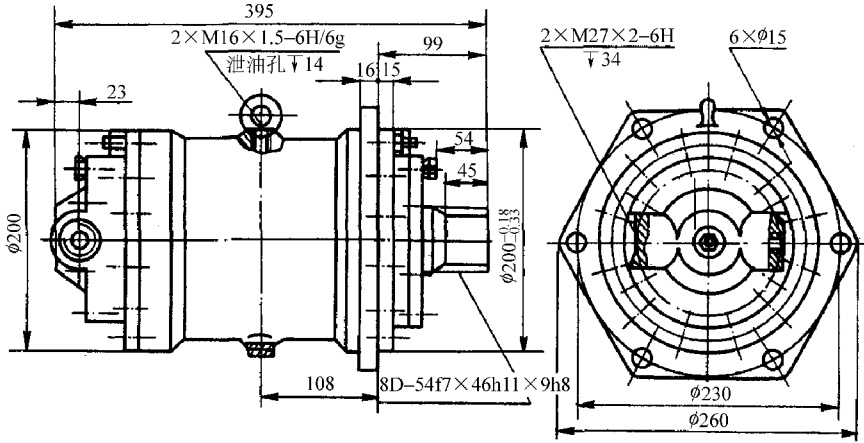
XM-F250F/XM-D320F 型马达外形尺寸
